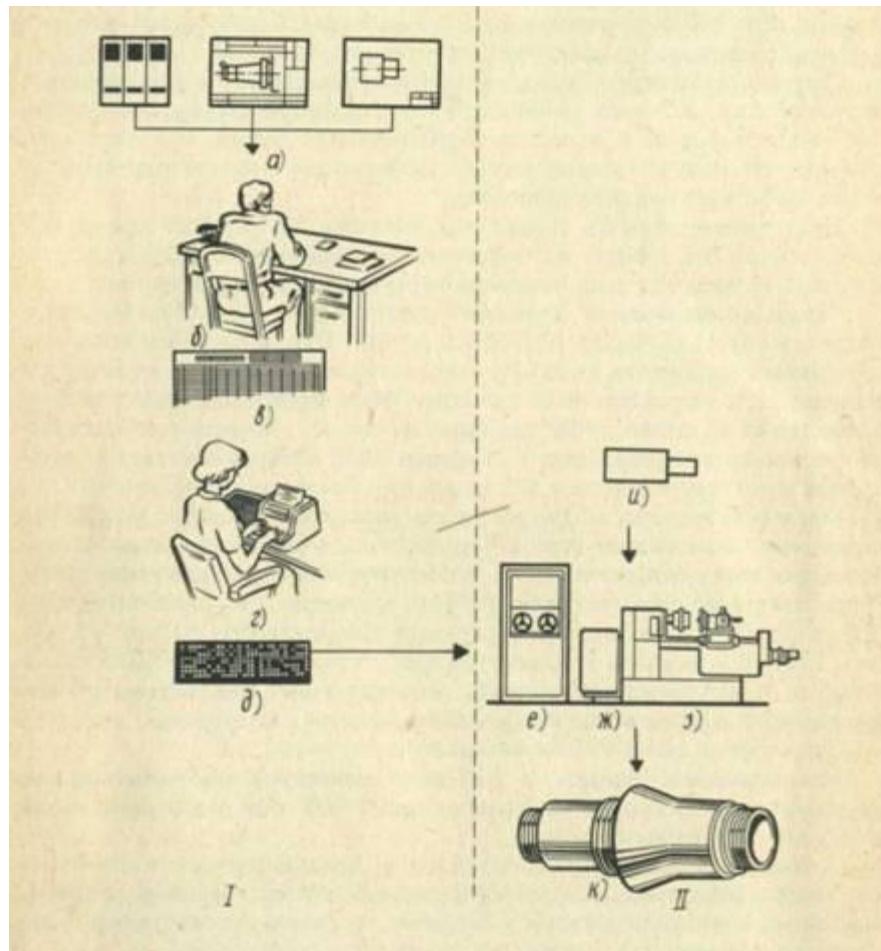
Етапи підготовки процесу обробки деталі на верстаті з ЧПК
